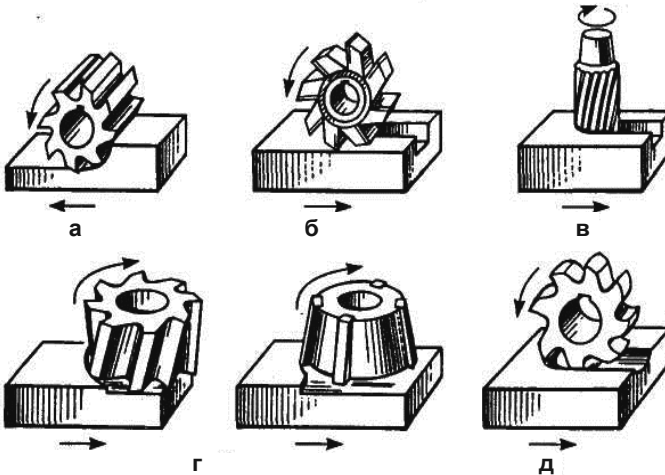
Основні види фрез: циліндрична (а), дискова (б), кінцева (в), торцева (г), фасонна (д)
